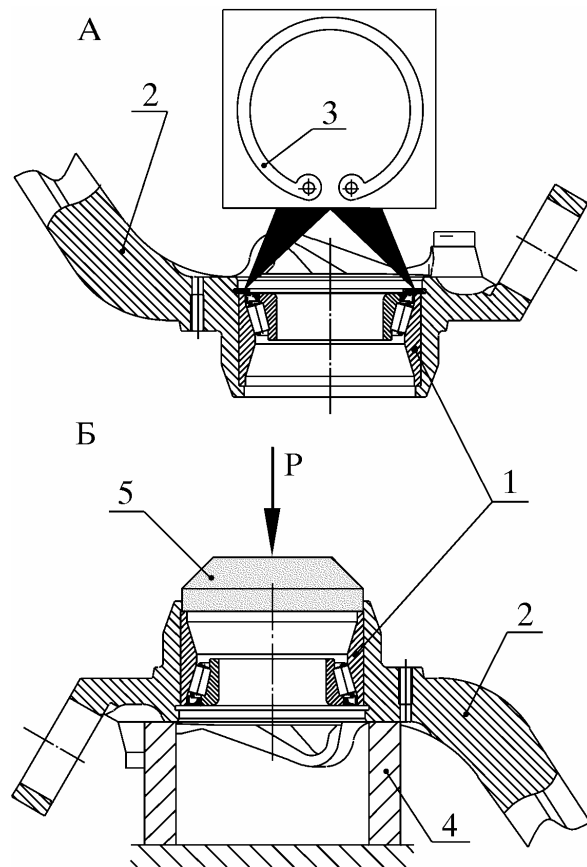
Снятие стопорного кольца и выпрессовка подшипника ступицы:
